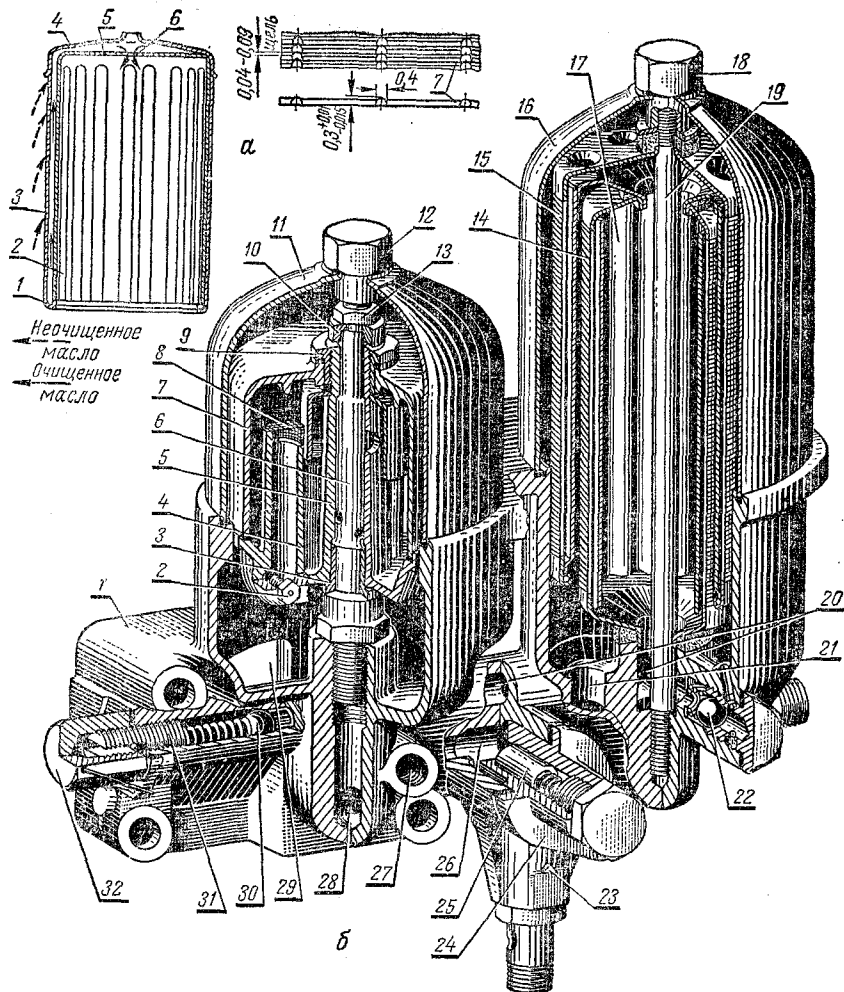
Фильтр грубой очистки и центробежный очиститель масла дизеля СМД-14:
